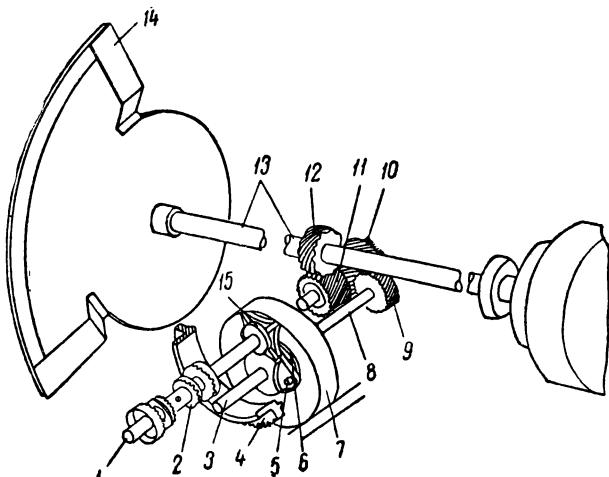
Кинематическая схема передачи движения малтийскому кресту:
